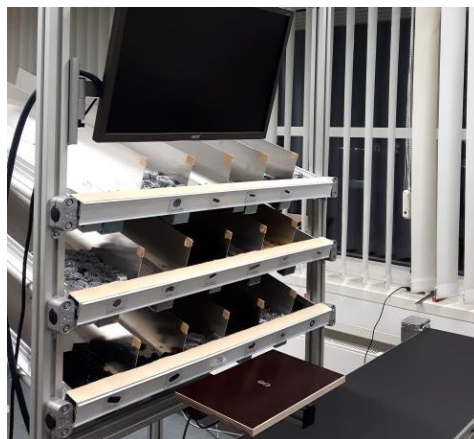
Versuchsaufbau mit Bauteile-Regal, Bildschirm und Montagefläche.
